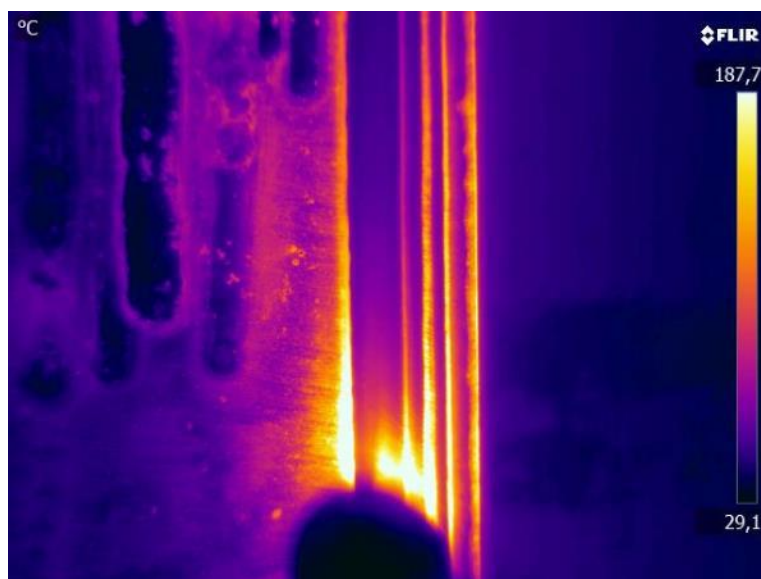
Imagen termográfica de un cordón de soldadura sin defectos a nivel macroscópico.
